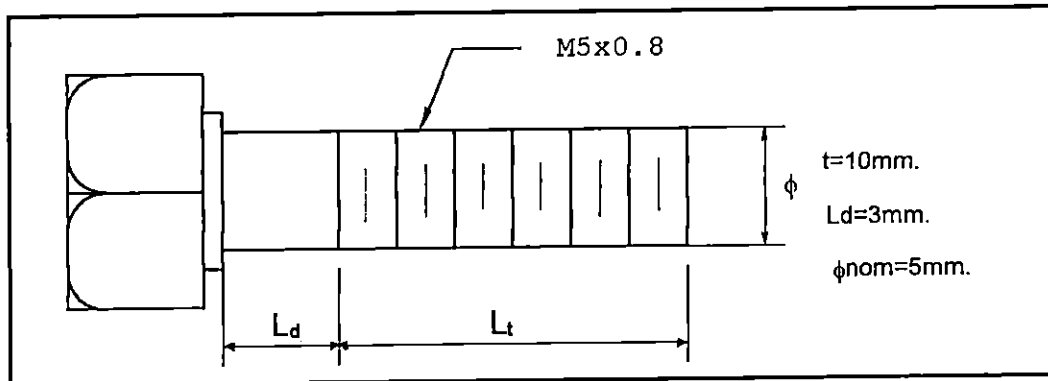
Tornillos para el sujetador de apoyo superior.
